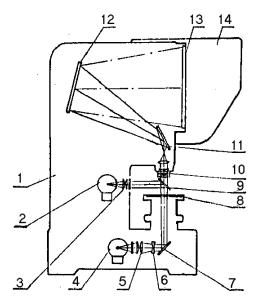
Проекционный аппарат 6CS: 1 — корпус; 2 — лампа подсветки; 3 — конденсатор; 4 — лампа подсветки; 5 и 6 — конденсаторные линзы; 7 — отражательное зеркало; 8 — предметный столик; 9 — полупрозрачное зеркало; 10 — объектив; 11 и 12 — отражательное зеркало; 13 — экран; 14 — теневой козырек
